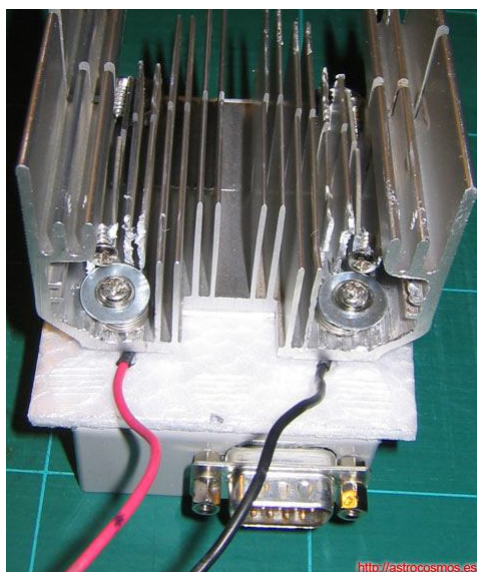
Detalle del conjunto de disipador instalado por la parte superior
